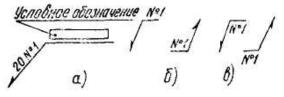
Обозначение одинаковых швов порядковыми номерами
